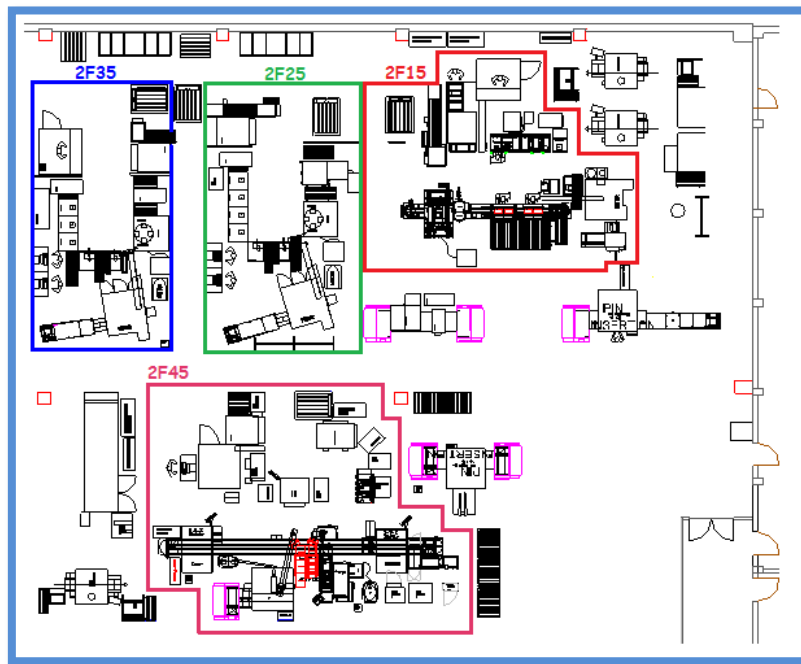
Layout da secção (identificação das células da montagem final)
